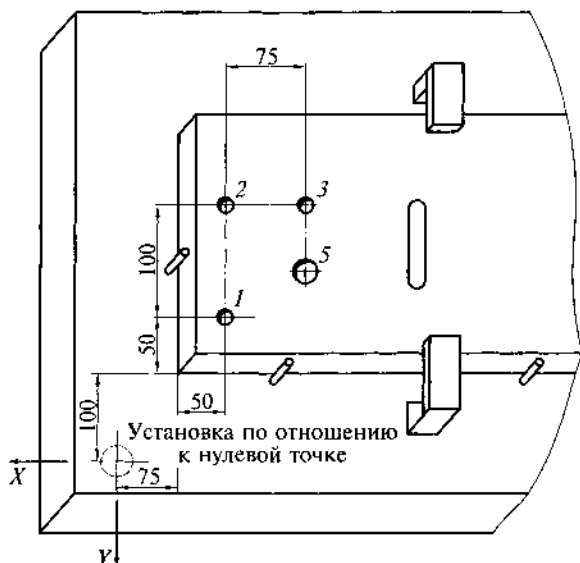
Базирование заготовки относительно нулевой точки станка
